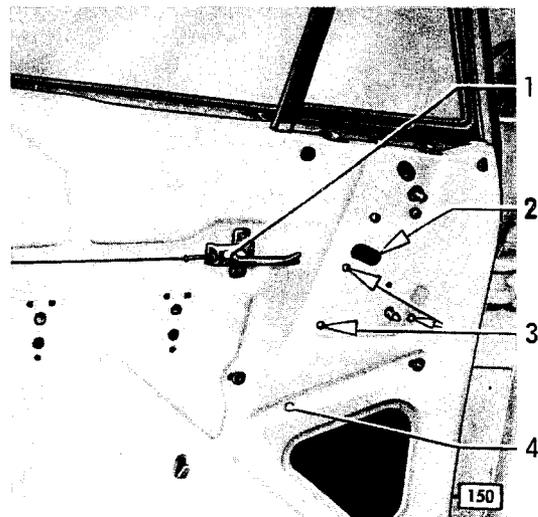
Befestigungsschrauben für Kurbelantrieb
